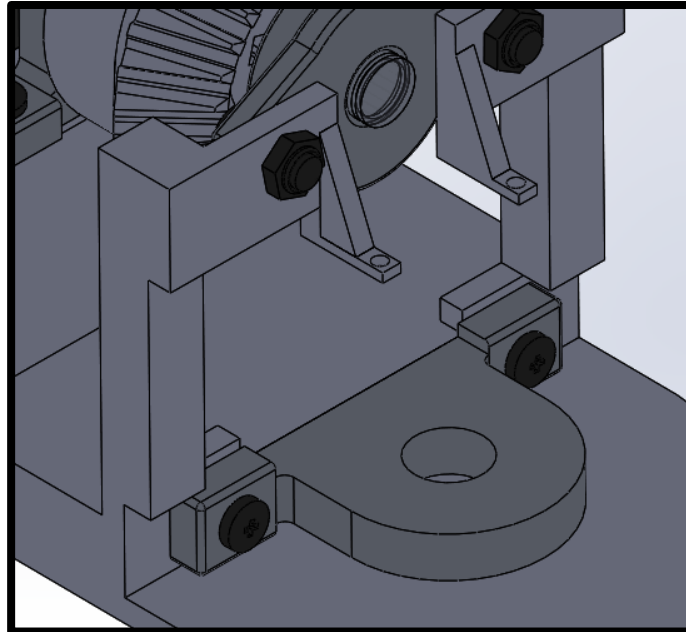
Detalle del montaje del rodamiento C en el bastidor. Fuente: Propia.
